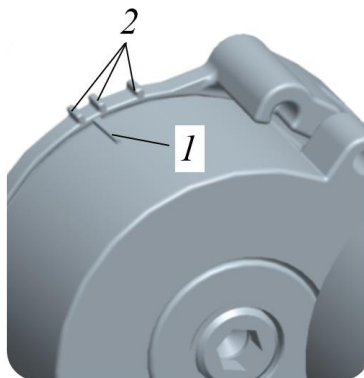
Процедура проверки натяжения ремня ЯМЗ-534
